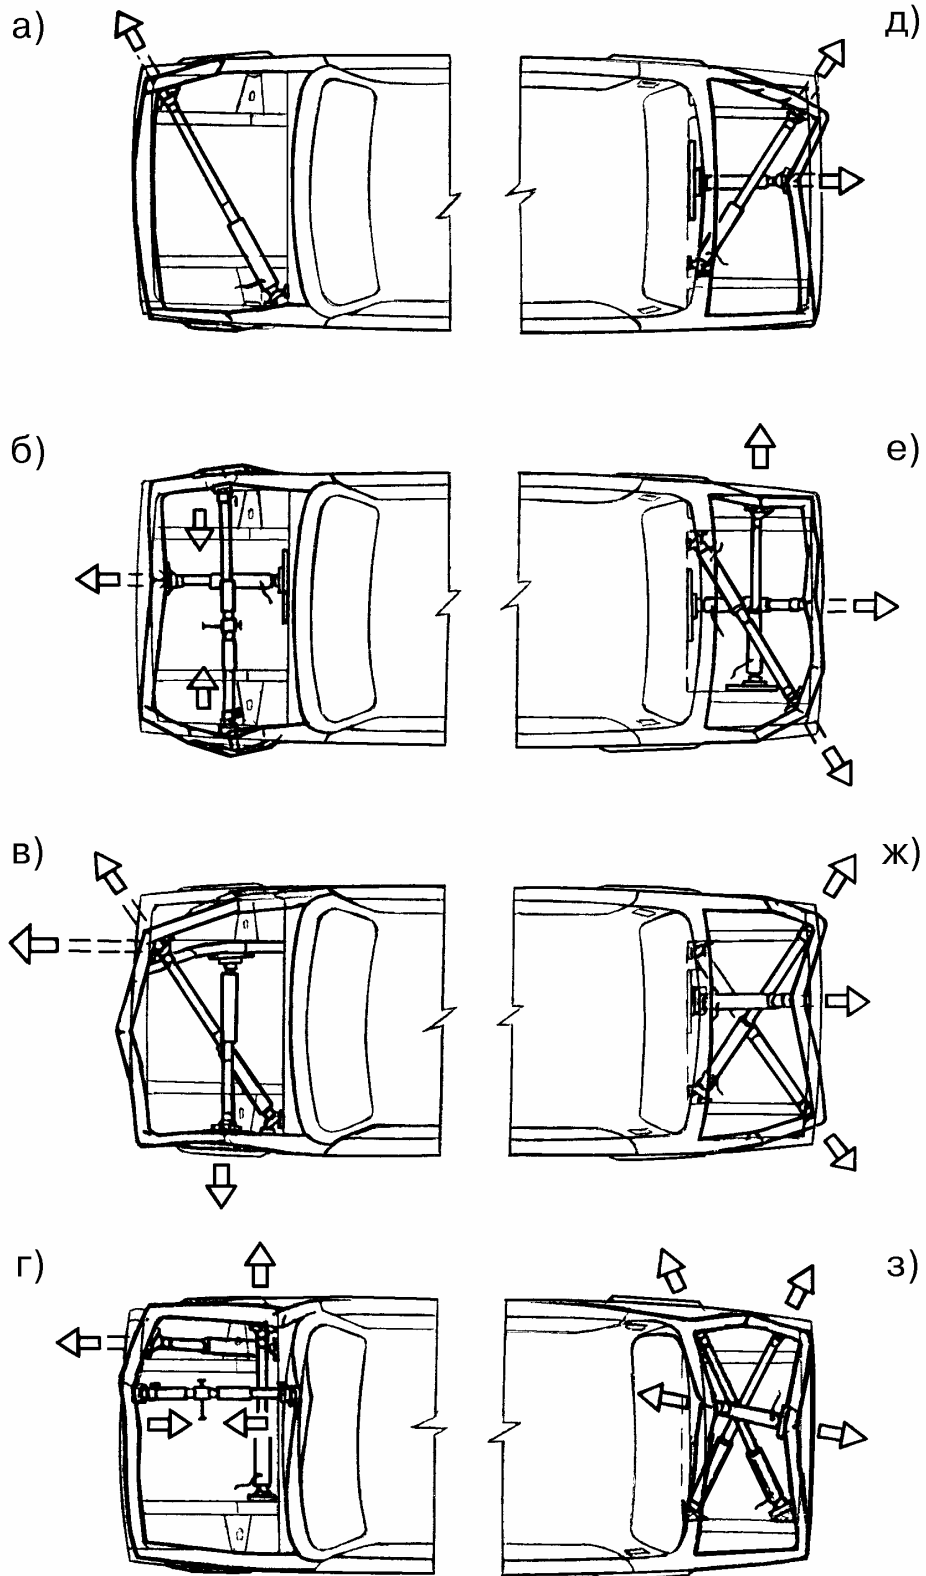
Варианты установки растяжек для устранения несложного перекоса проема капота или проема крышки багажника.
